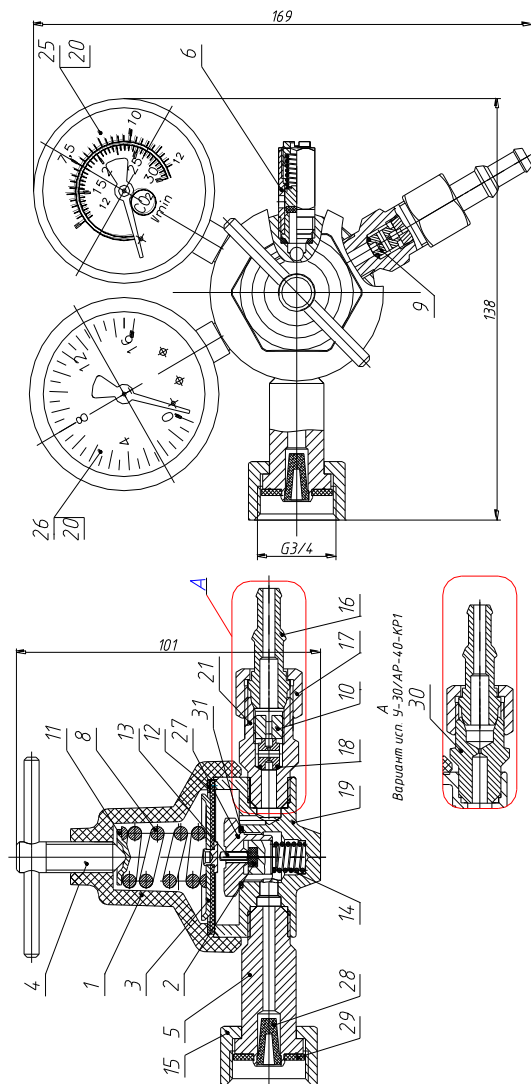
Регулятор расхода газа баллонный одноступенчатый крупногабаритный:
